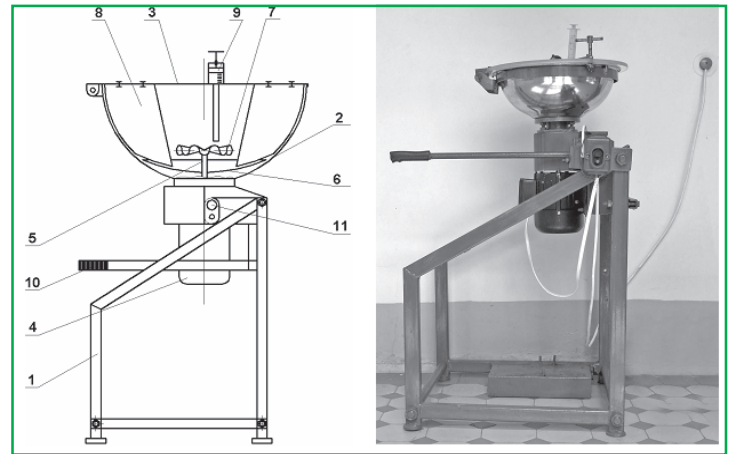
Схема макетного зразка пристрою для протруювання насіння: 1 – рама; 2 – робоча камера; 3 – відкидна кришка; 4 – електродвигун; 5 – вертикальний вал; 6 – тарілчастий диск; 7 – диск-розприскувач; 8 – лопаті-ворушилки; 9 – ємкість-дозатор; 10 – важіль; 11 – пускач.
